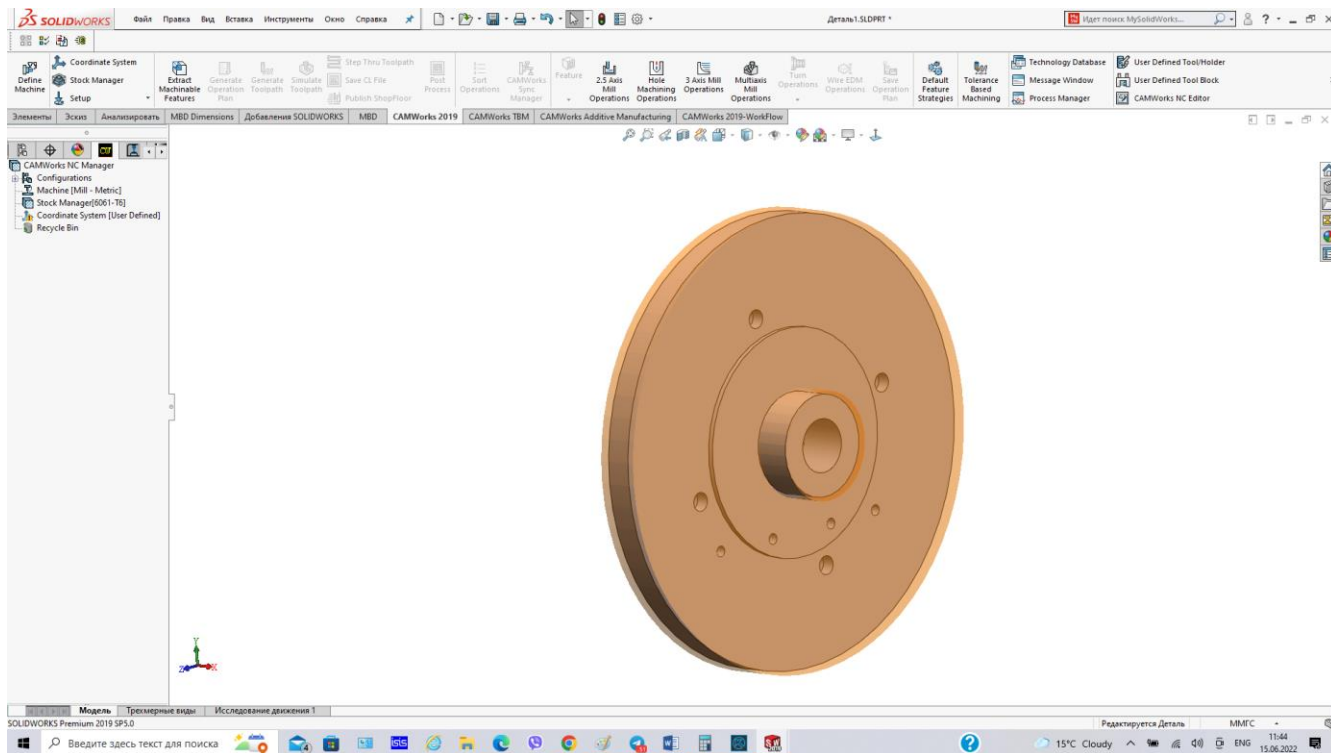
Деталь та заготовка в системі Solid-CAM
